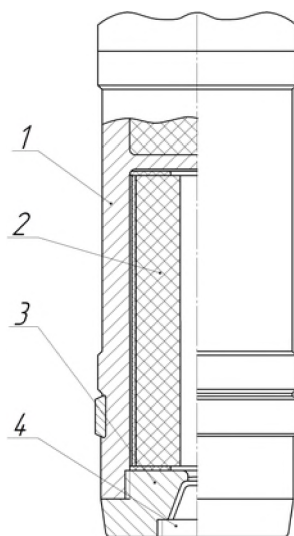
Реактивный двигатель APC: 1 – корпус; 2 – топливный заряд; 3 – сопловой блок; 4 – замедлительно-воспламеняющее устройство
